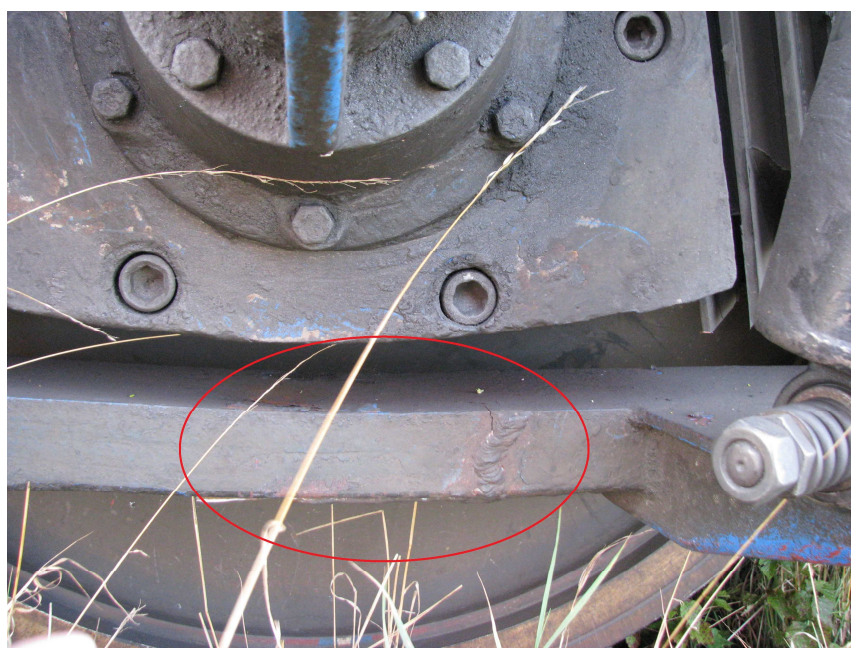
sudură, fisură și amprente de lovituri în placa de gardă
